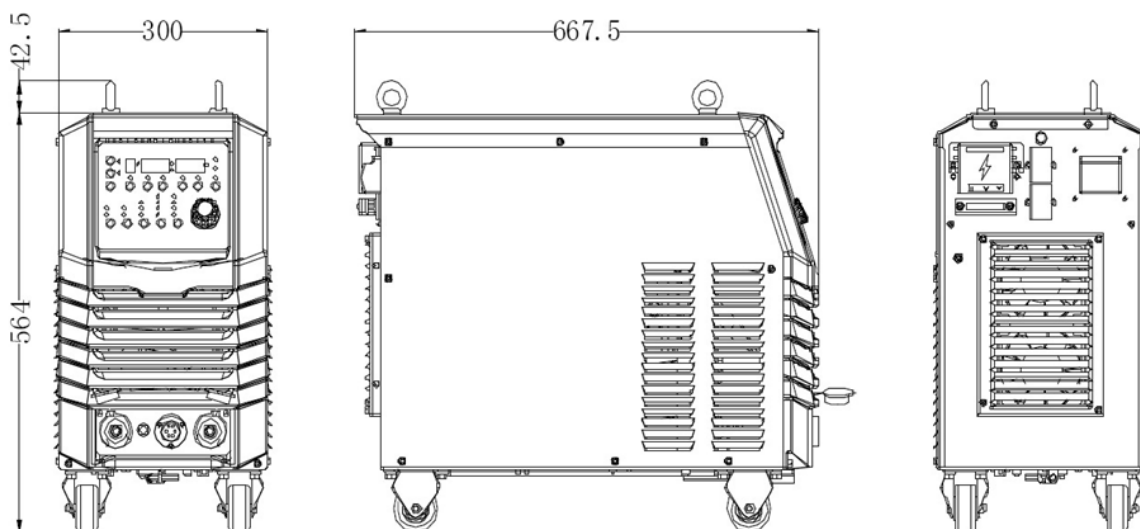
Габаритные размеры сварочного источника питания
